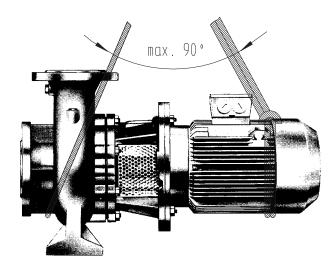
Hebezeug befestigen an Pumpenaggregat
